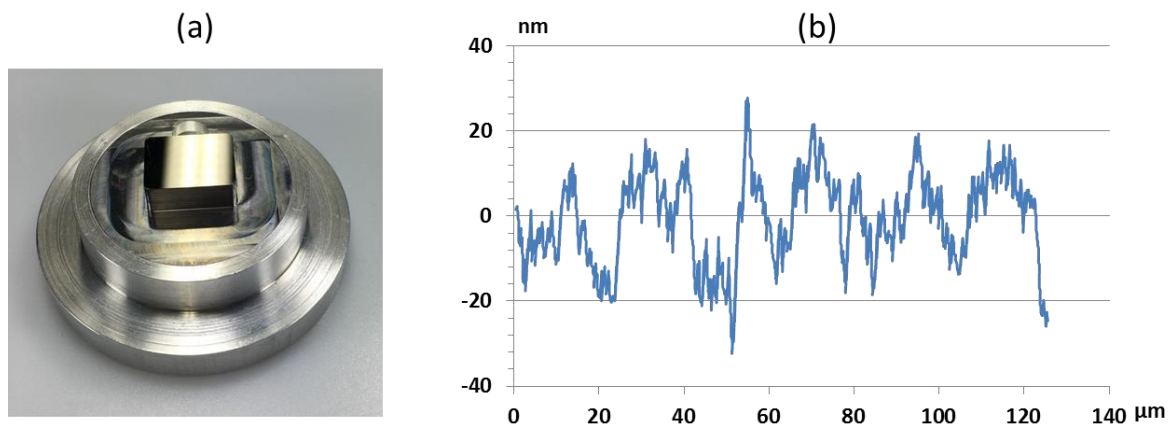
a) Werkzeugeinsatz mit Planfläche nach dem Fly-Cutting-Prozess b) Rauheitsprofil gemessen mittels WLI [32]
